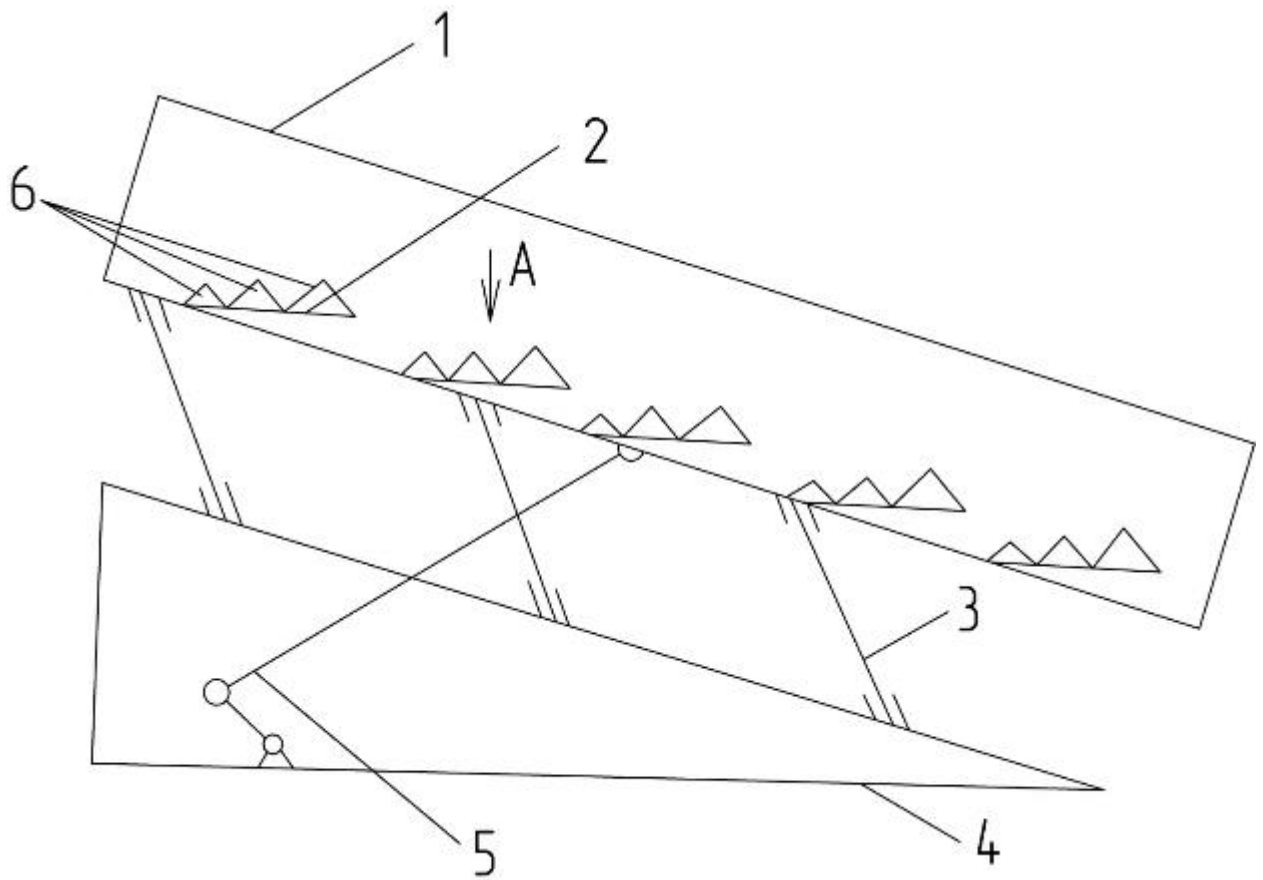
Схема вібраційного змішувача безперервної дії з конічними робочими поверхнями: 1 - змішувальний орган; 2 – перемішувачі елементи; 3 - ресори; 4 - рама; 5 — ексцентриковий механізм; 6 - конічні робочі поверхні.
